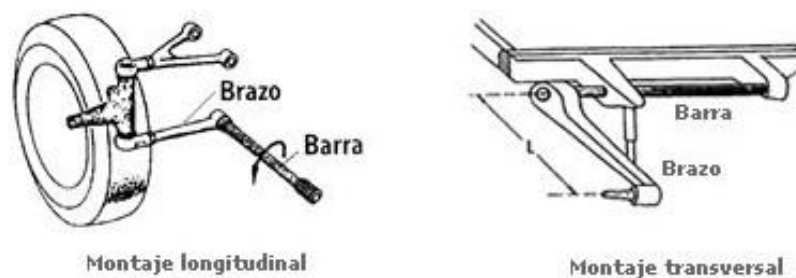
Montaje longitudinal y transversal de barras de torsión [9]
